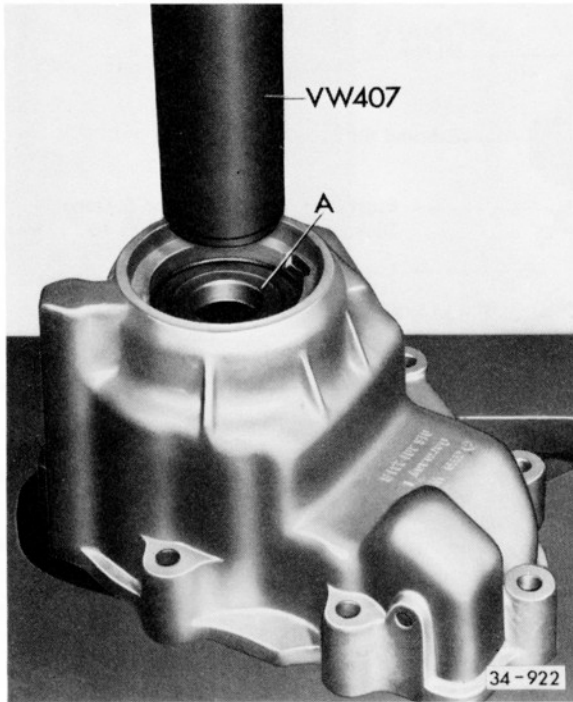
Kugellager aus Deckel für Lagerschild auspressen
